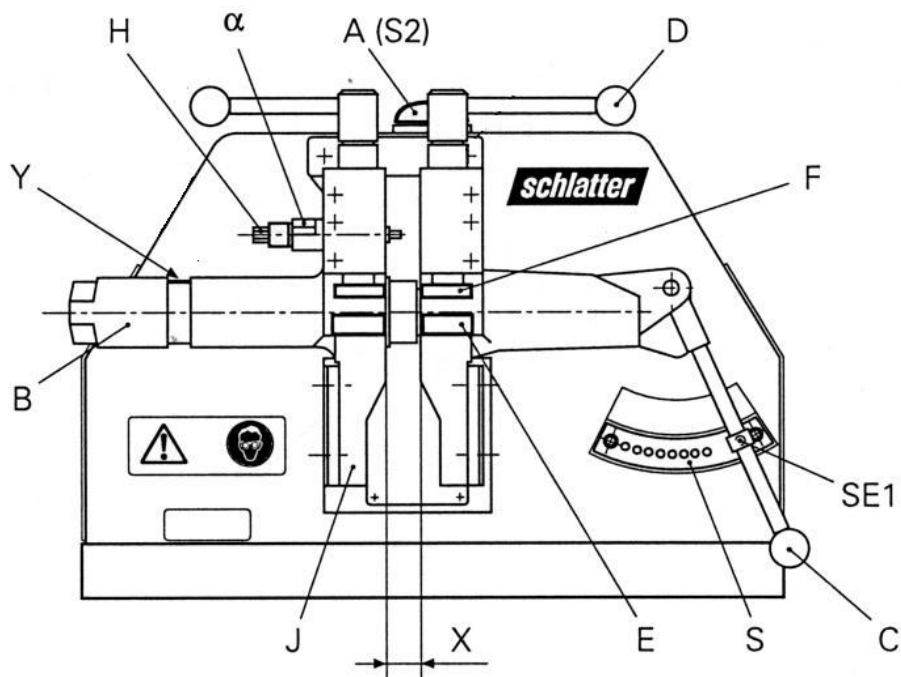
Máquina de soldar a topo tipo M , tabela de ajuste
